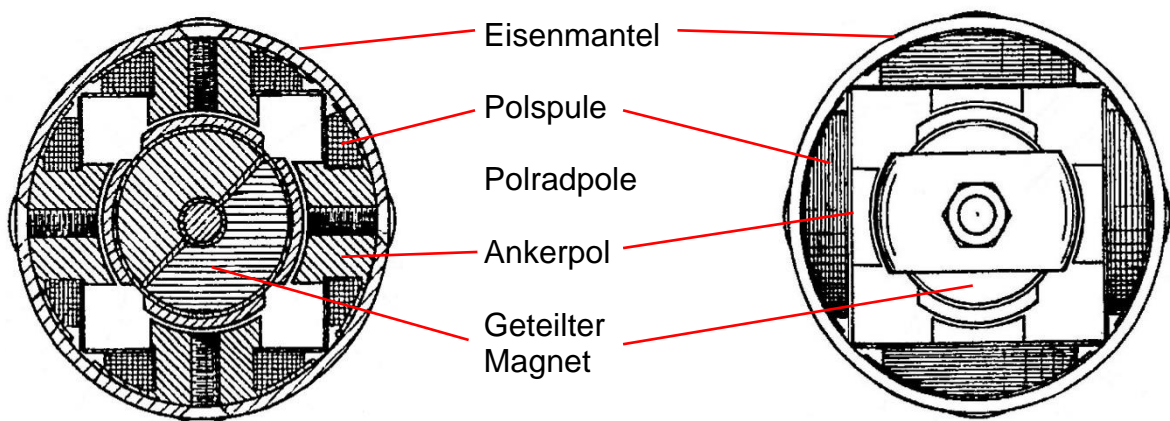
a) Querschnitt durch die Ebene mit den Polschrauben, b) Stirnansicht des Generators
